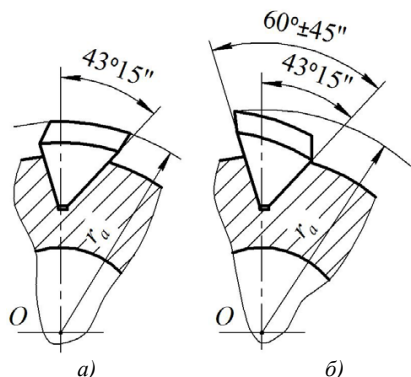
Установка зубчатых реек в корпусе сборной фрезы в технологическом (а) и рабочем (а) положениях
